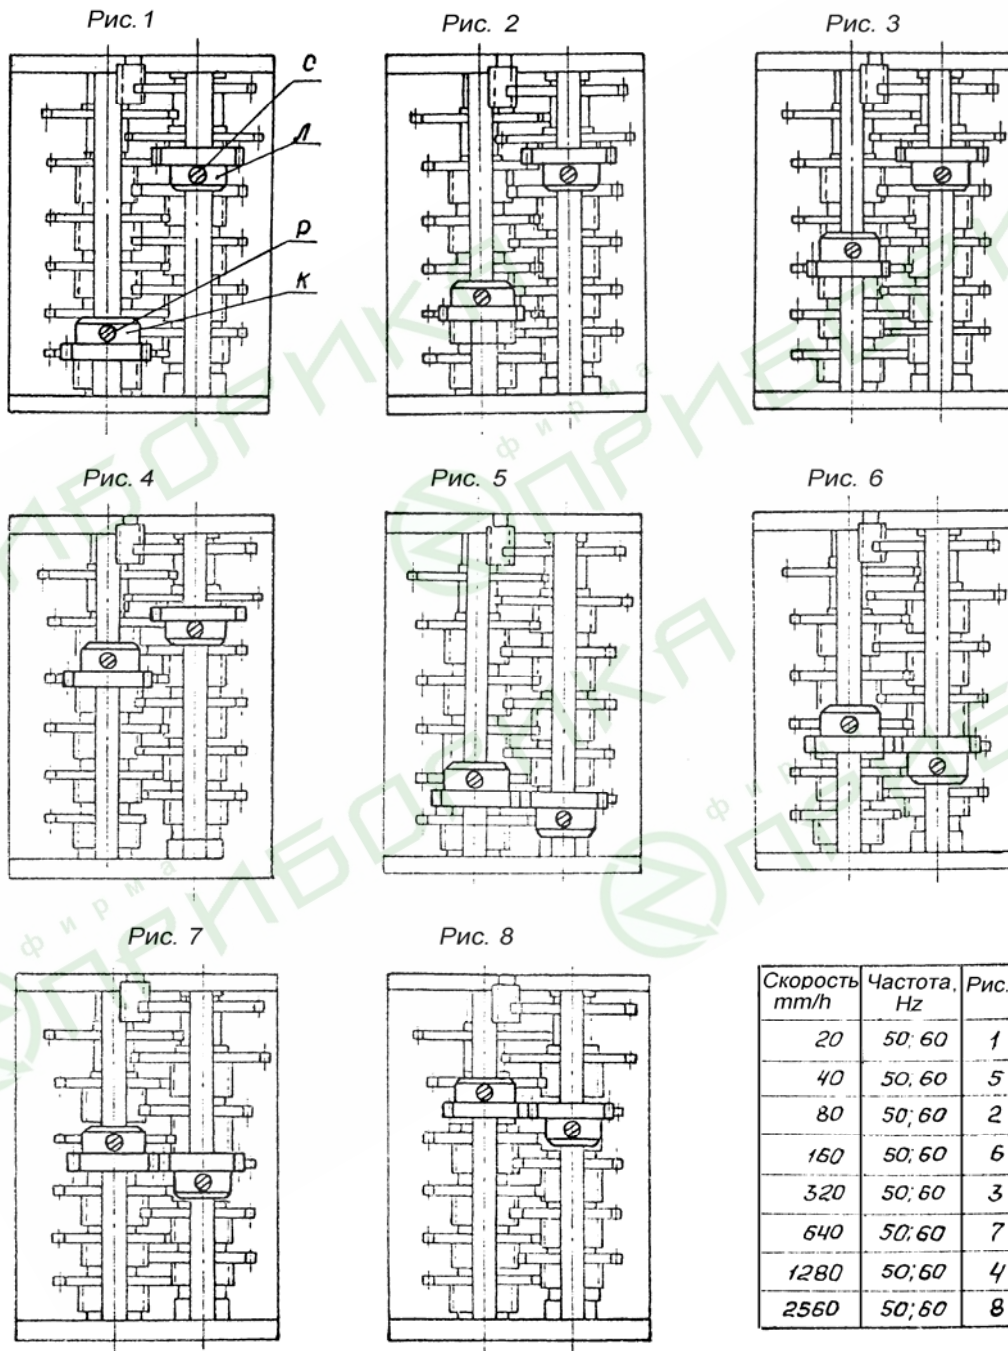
Схемы кинематические редуктора лентопротяжного механизма:
